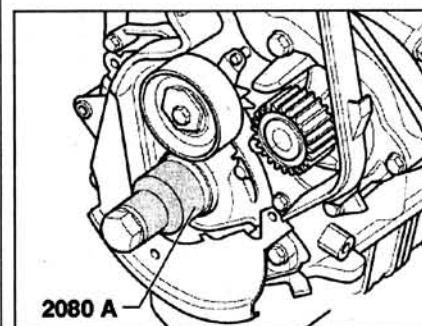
Запрессуйте сальник до упора с помощью приспособления 2080A и центрального болта вибродемпфера.
